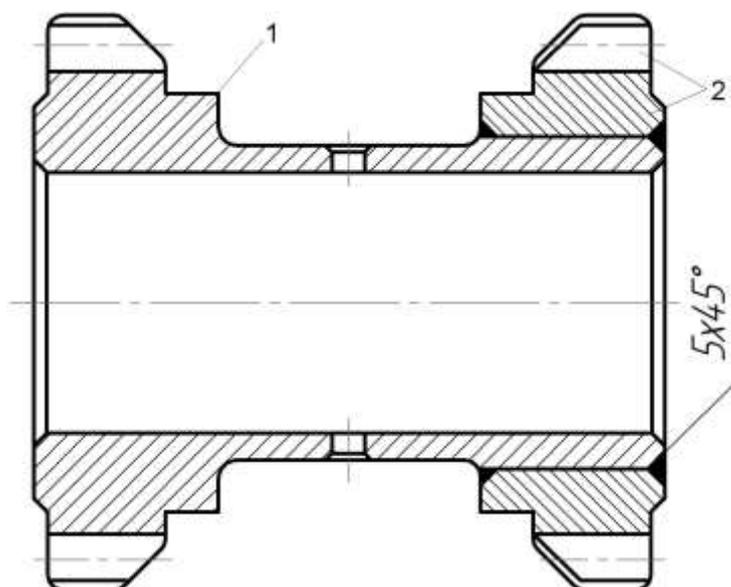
Восстановление блока шестерен коробки передач постановкой зубчатого венца: 1 – шестерня; 2 – венец
